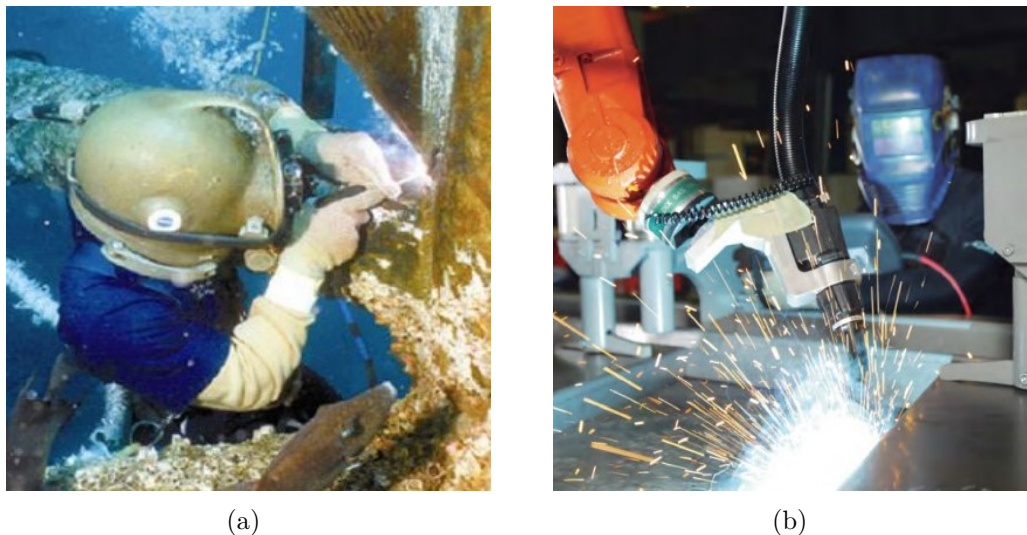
Exemplo de diferentes processos de soldagem. a) Soldagem subaquática (BRACARENSE, 2016) e b) Soldagem MIG robótica (ESAB, 2020)
